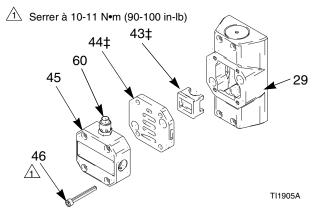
Couvercle, siège et coupelle de la vanne d'air
